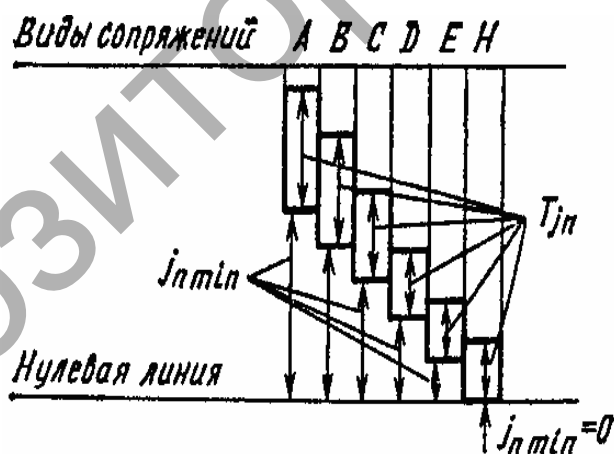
Схема расположения полей допусков  $T_{jn}$  для принятых видов сопряжений зубьев зубчатых колес
